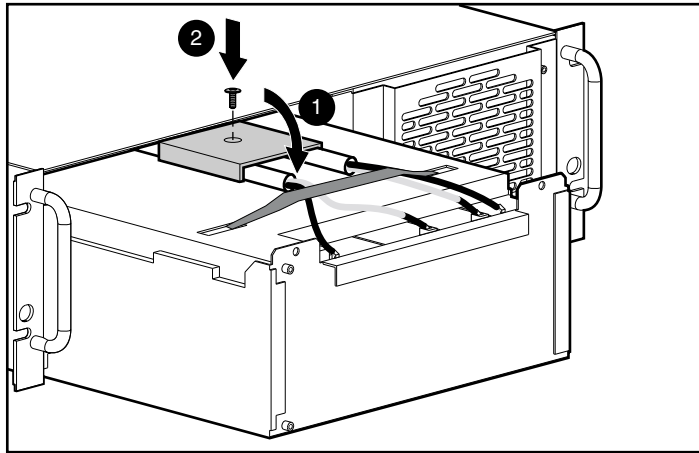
Anbringen der Zugentlastung des Akkukabels
